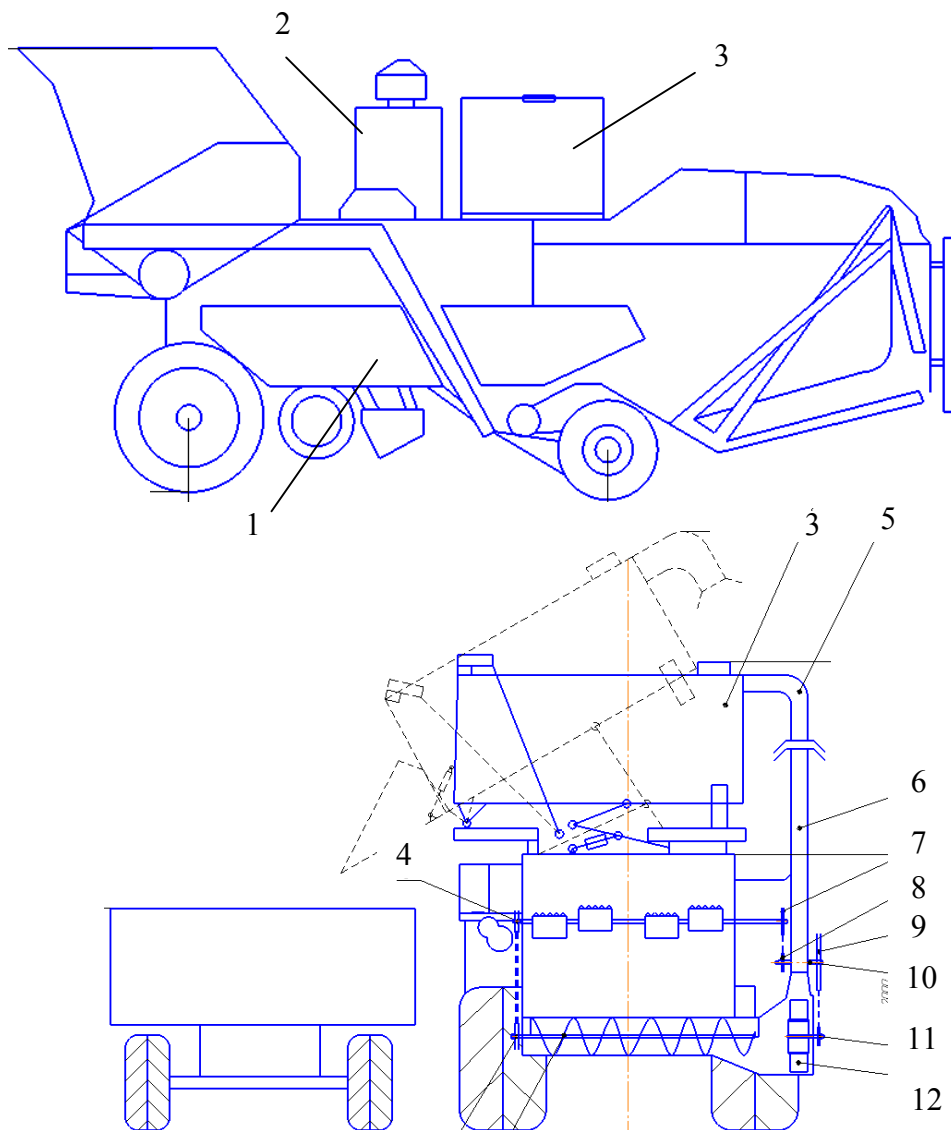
Зерноуборочный комбайн с системой раздельного сбора семенного зерна и зернового вороха:
